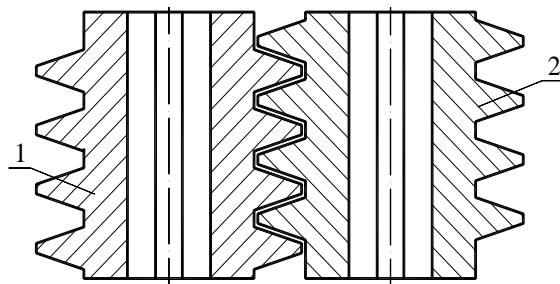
Валковий перероблювальний пристрій із зубчастими валками:
